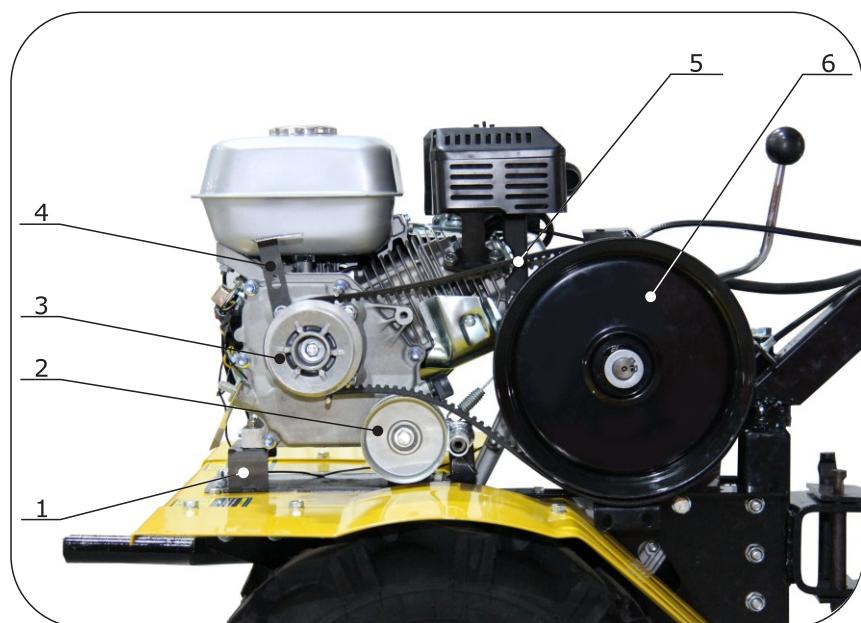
Мотоблок. Вид слева (защитный кожух снят).
